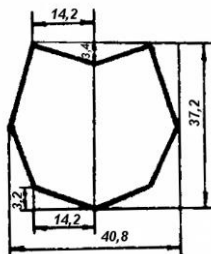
Схема побудови лекала підкладки бічної кишені штанів з відрізним блокуванням
